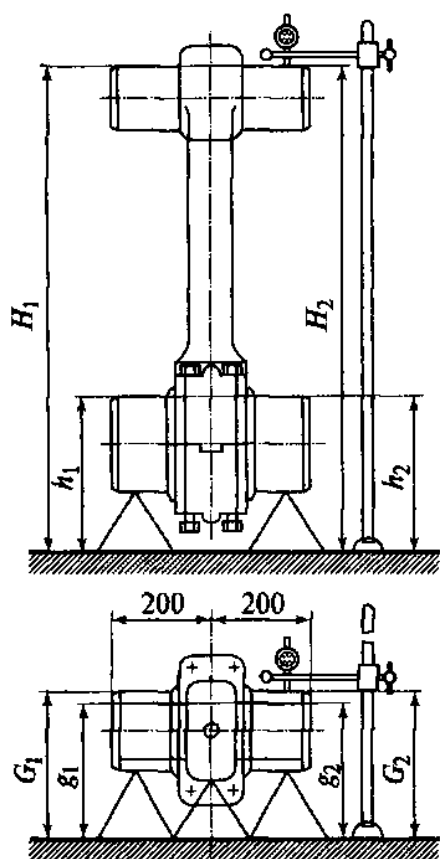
Схема проверки индикаторным приспособлением параллельности и скрещивания осей отверстий головки шатуна:
